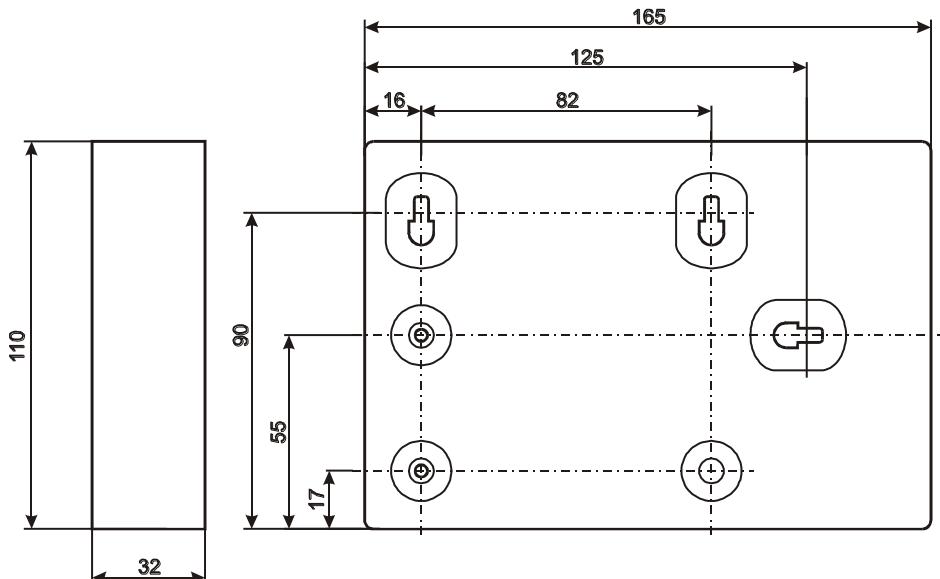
Внешний вид и габаритные размеры БРЛ в исп. IP20
